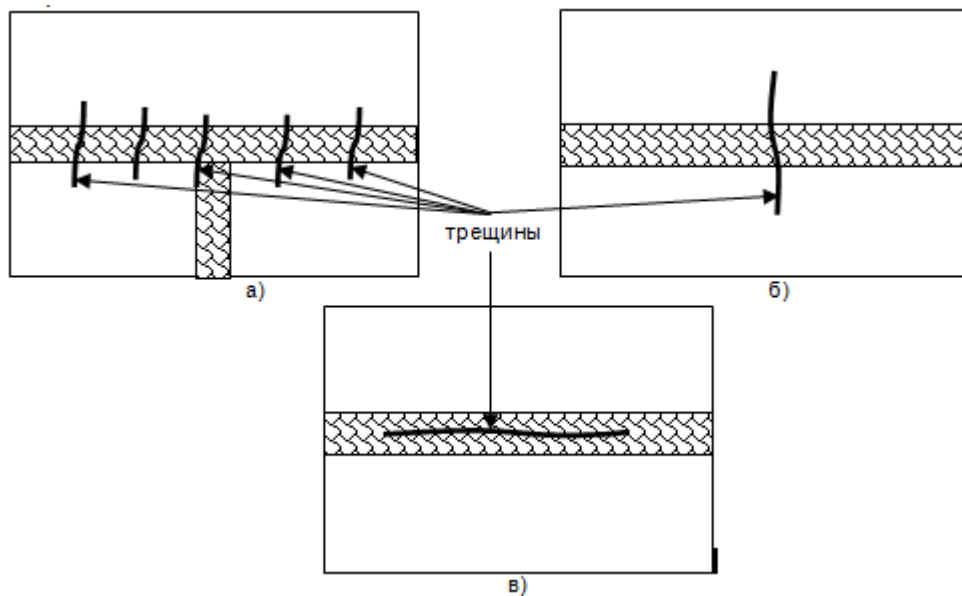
Схема расположения трещин на образцах сварных соединений с продольным и пересекающимися сварными швами после испытаний на КРН.
